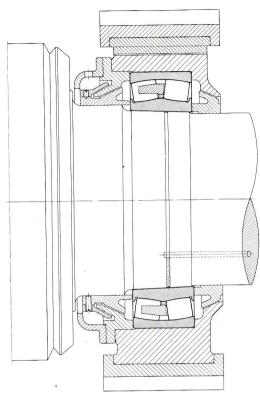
Disposición de rodamientos en una calandra para plásticos provista de mecanismo para poner los cilindros oblicuamente
